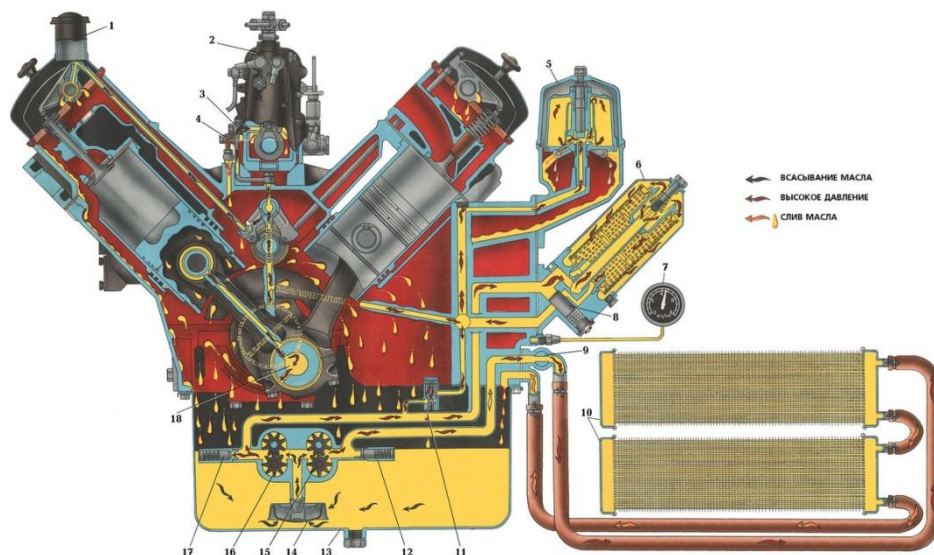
Система смазки двигателя внутреннего сгорания
